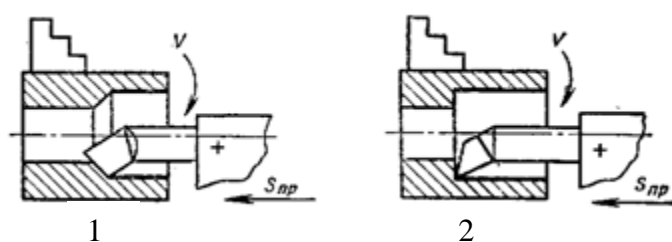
Эскизы обработки внутренних цилиндрических поверхностей:
